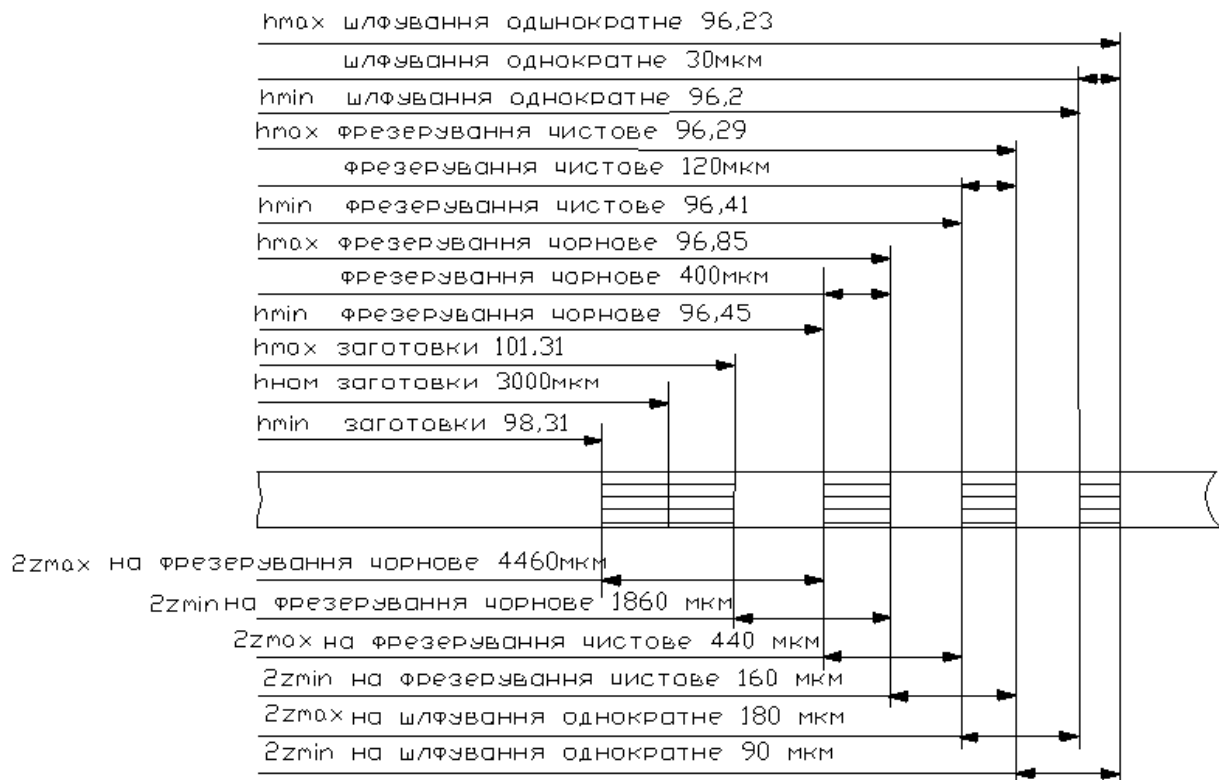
Схема розташування полів допусків та припусків на поверхню
